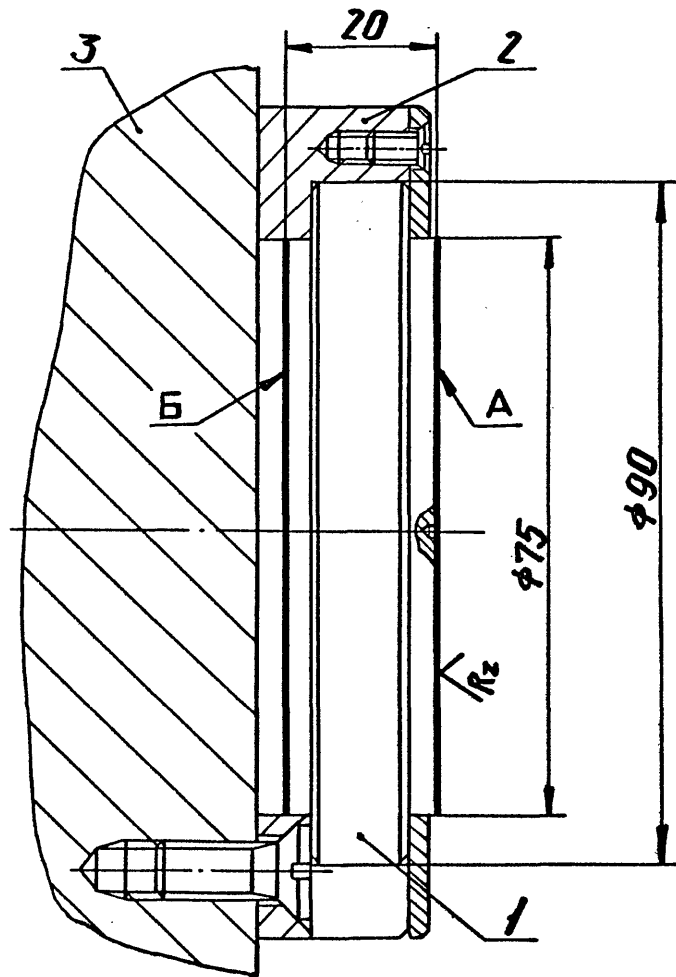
Образец и приспособление для его крепления на планшайбе стенда.
